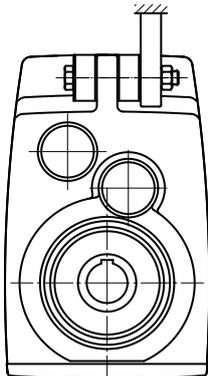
Резиновые амортизаторы (опция G или VG) на редукторах с параллельными валами
